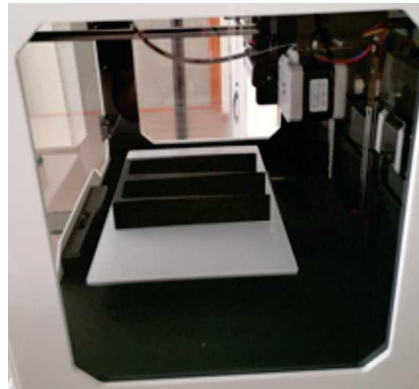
La impresora 3D y una cavidad en V en diente de sierra durante la impresión.
